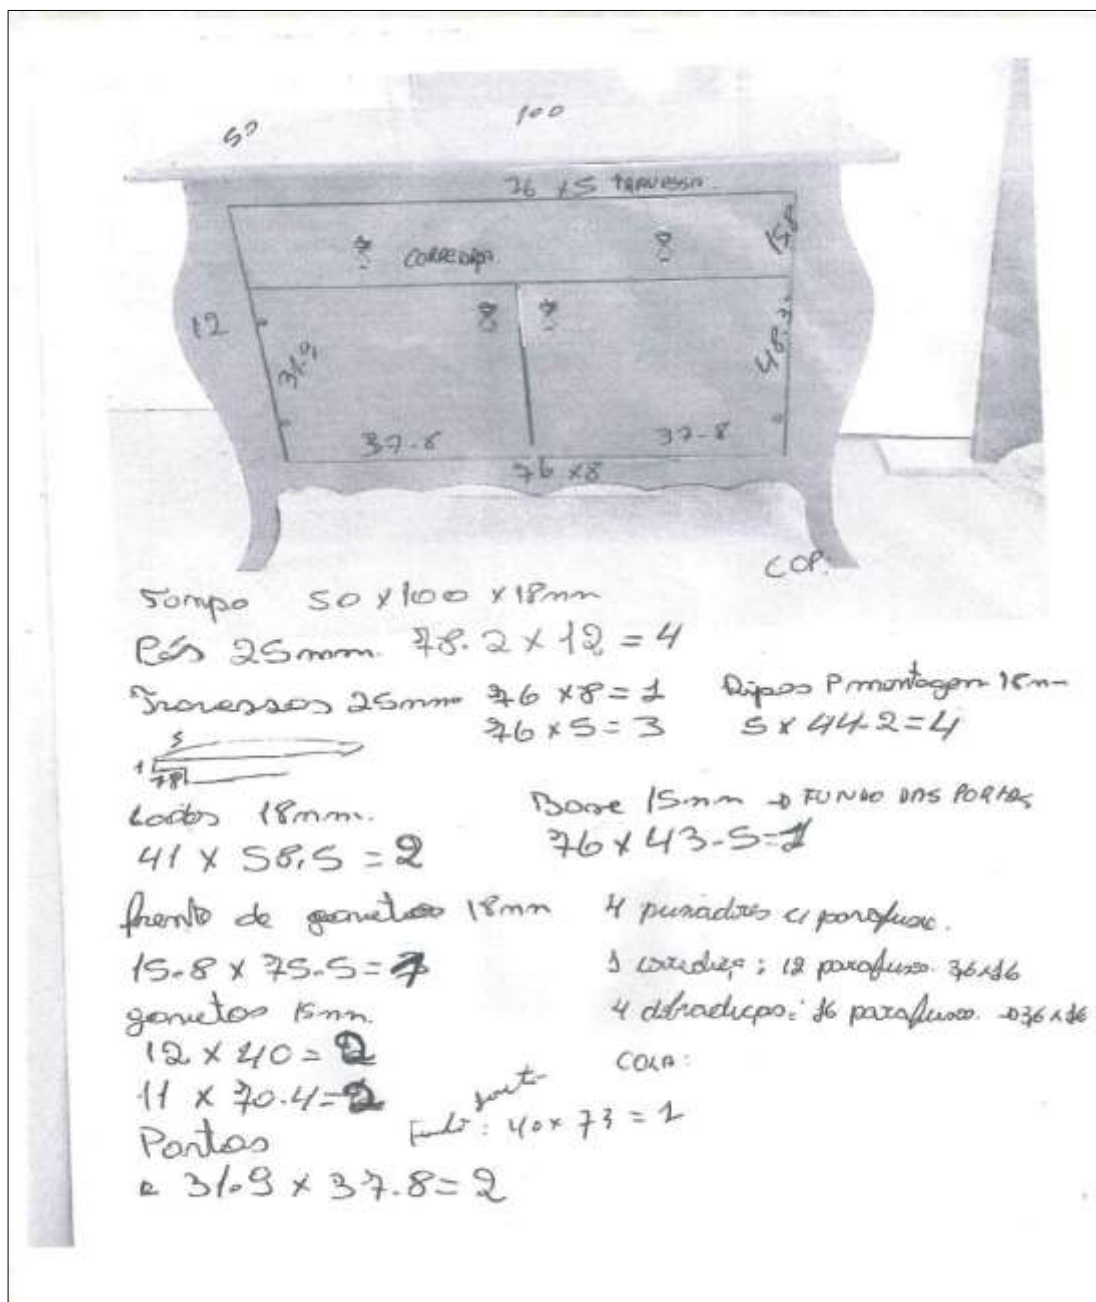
Desenho técnico da COP (Cômoda Pequena)
